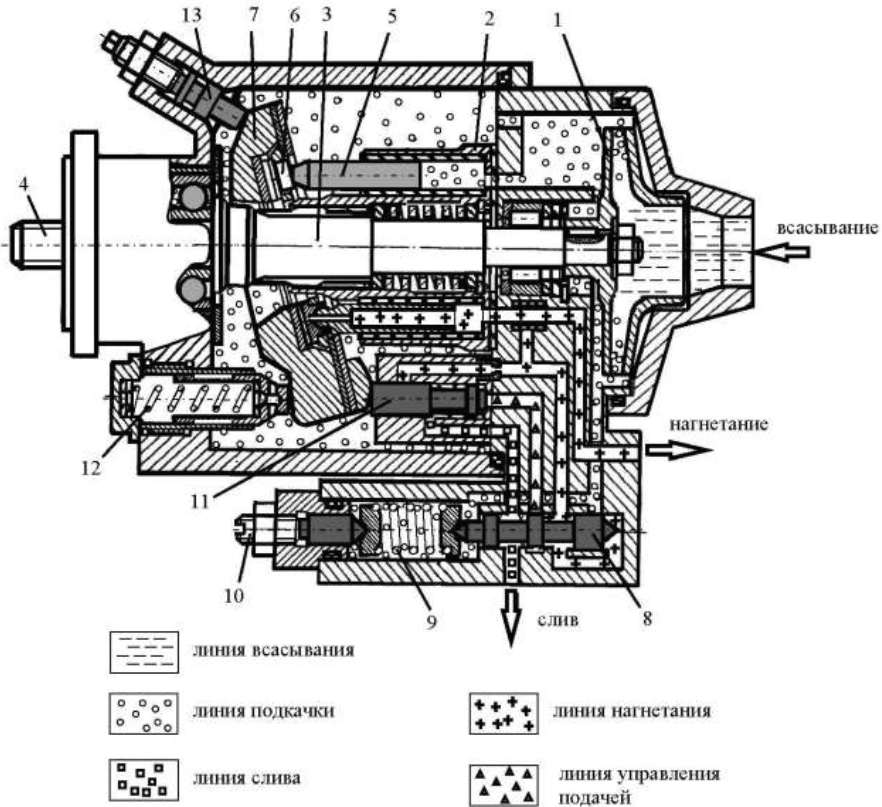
Принципиальная схема гидравлического насоса аксиально-плунжерного типа, где 1- центробежный насос подкачки; 2- блок цилиндров; 3- приводной вал; 4- рессора; 5- плунжер; 6- башмак; 7- опорная шайба; 8- золотник; 9, 12- пружины; 10- регулировочный винт; 11- поршень; 13- упор
